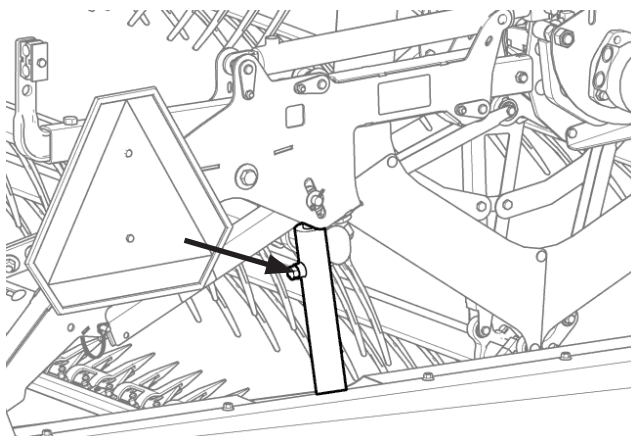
Отверстие для стравливания воздуха из цилиндра мотовила
